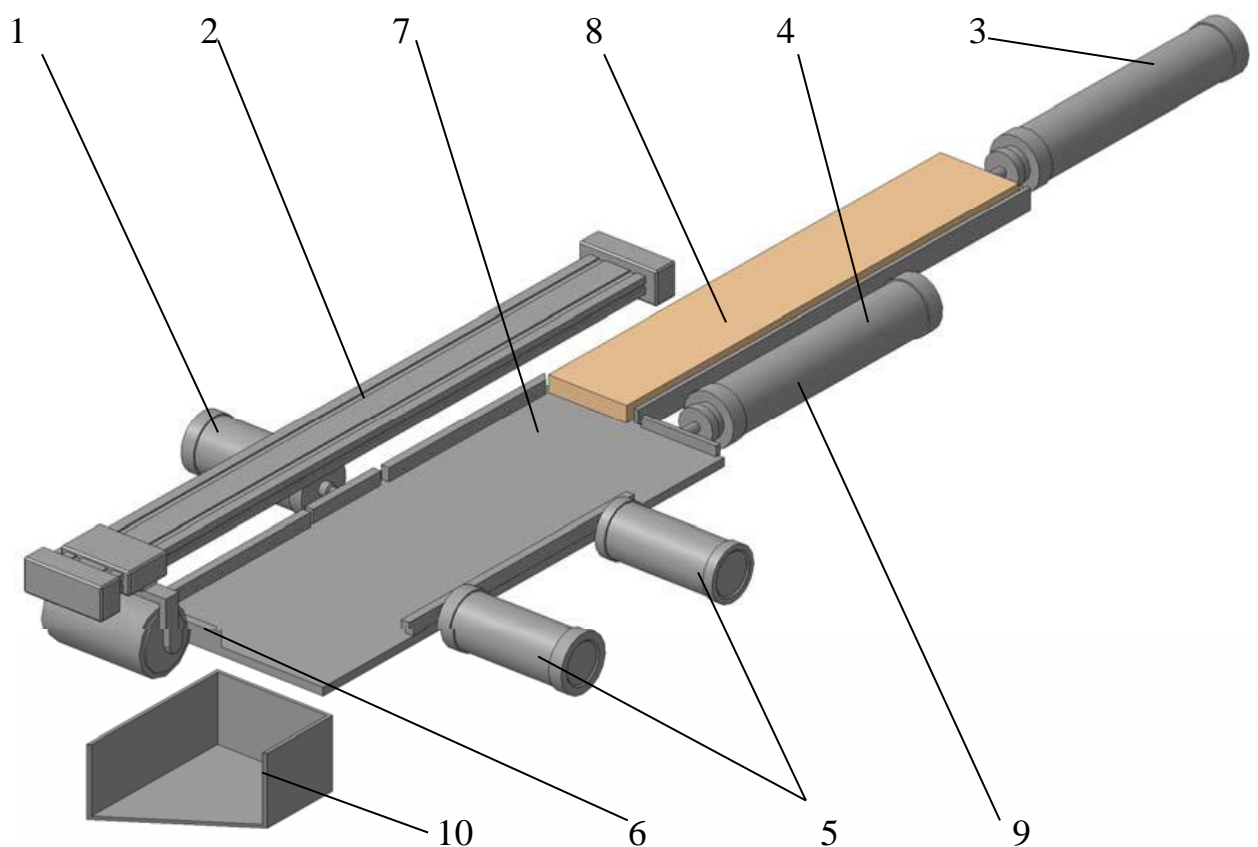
Верстат для шліфування деревини модуль 2 повертається в початкове положення. Привід 5 повертається в початкове положення. Циліндр 1 зрушує дошку з упорів, після чого циліндр 4
